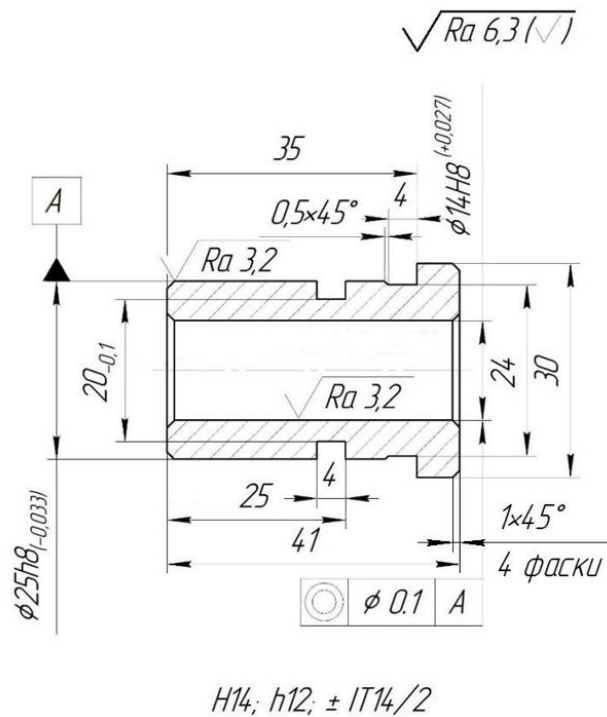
Фрагмент робочого кресленика втулки
